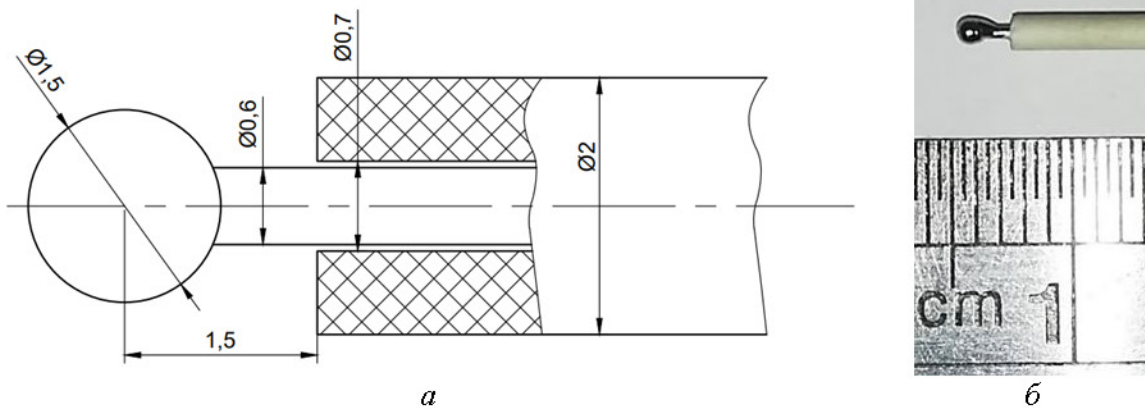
Чертеж (а) и внешний вид зонда (б)
